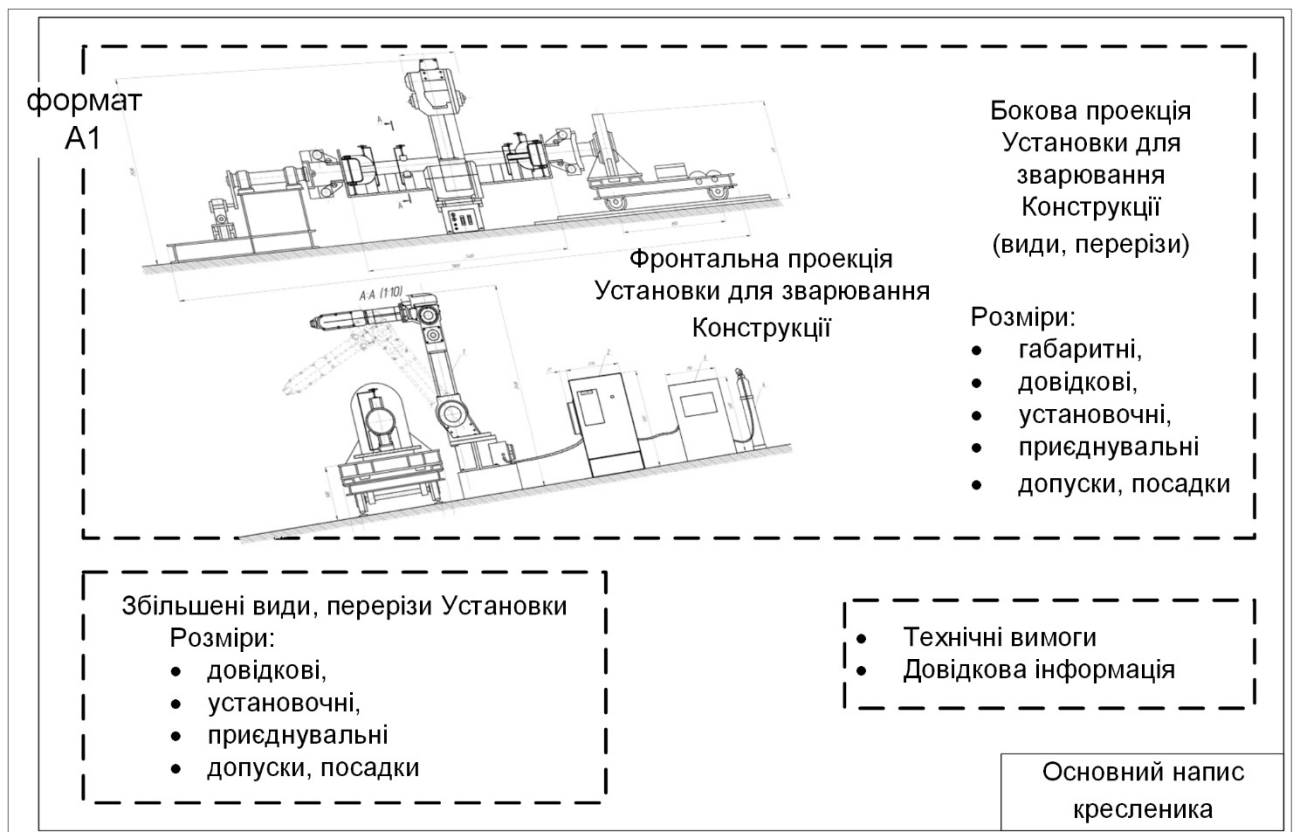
Рекомендована структура кресленника «Установка для зварювання складеної до зварювання {Конструкції}. Складальний кресленник»
